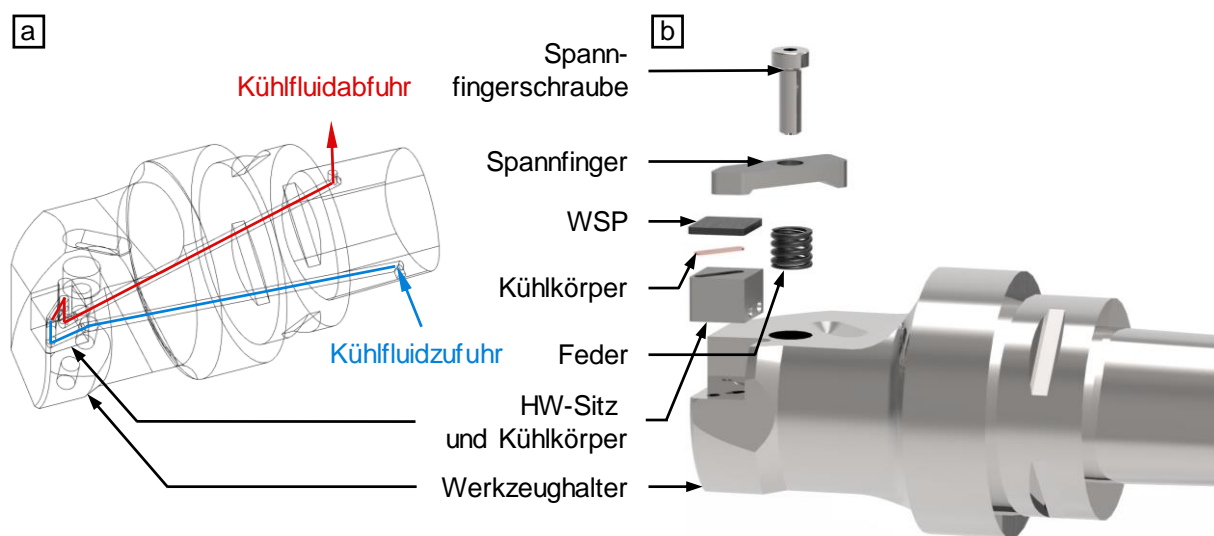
Erster Vorentwurf; a) Schnittansicht; b) Explosionsansicht
